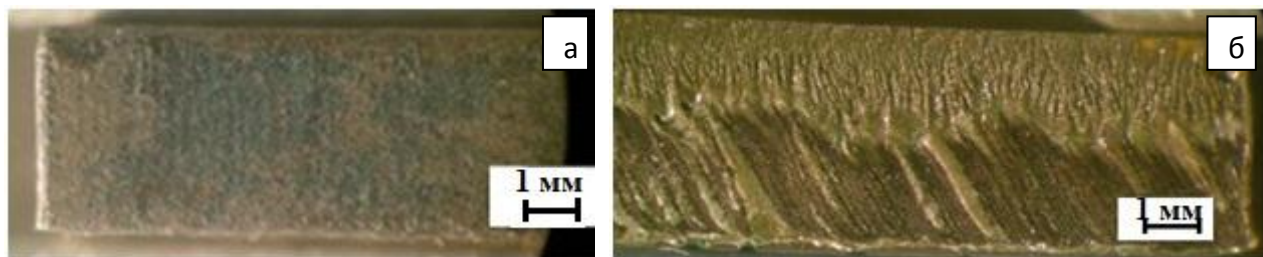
Внешний вид поверхности реза стали Ст3 (а) и стали 12Х18Н10Т (б)
